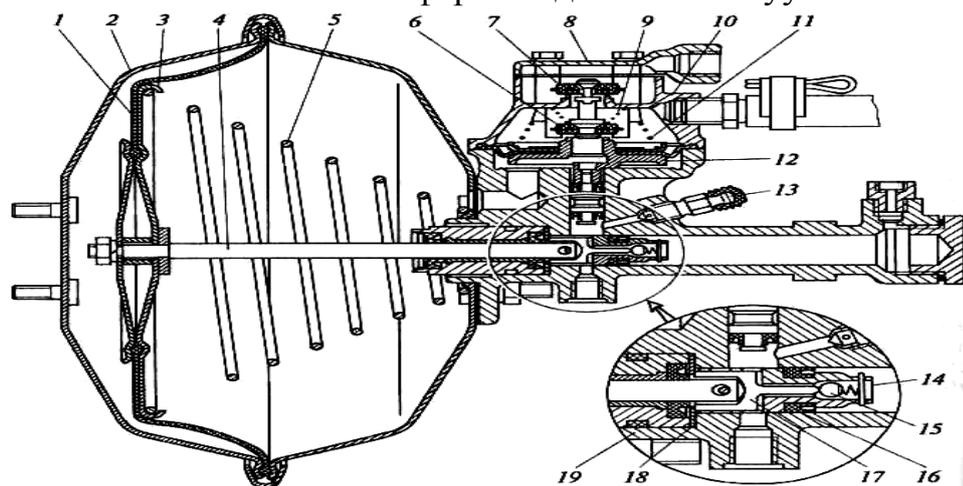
Гидровакуумный усилитель тормозного привода: 1 — ; 2 — корпус; 3 — тарелка диафрагмы; 4 — толкатель поршня; 5 — пружина; 6 — вакуумный клапан; 7 — атмосферный клапан; 8 — крышка корпуса; 9 — пружина атмосферного клапана; 10 — корпус клапана управления; 11 — пружина клапана; 12 — поршень клапана; 13 — ; 14 — поршень; 15 — клапан поршня; 16 — манжета поршня; 17 — толкатель клапана; 18 — упорная шайба поршня; 19 — цилиндр
